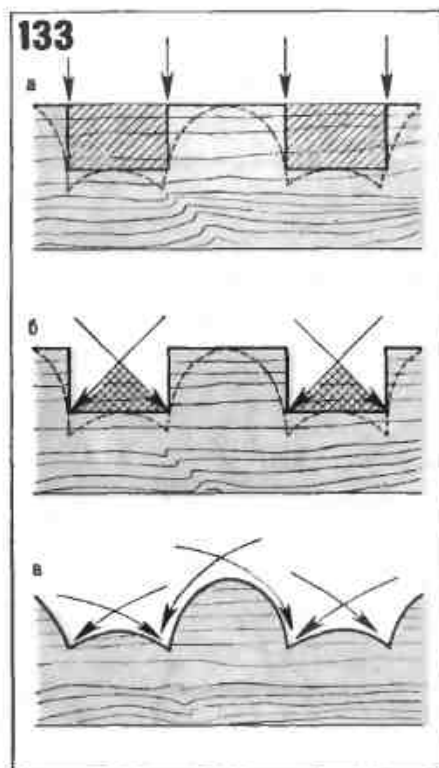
Техника выполнения плоскорельефной резьбы с подушечным фоном (стрелками показано направление движения инструмента):
